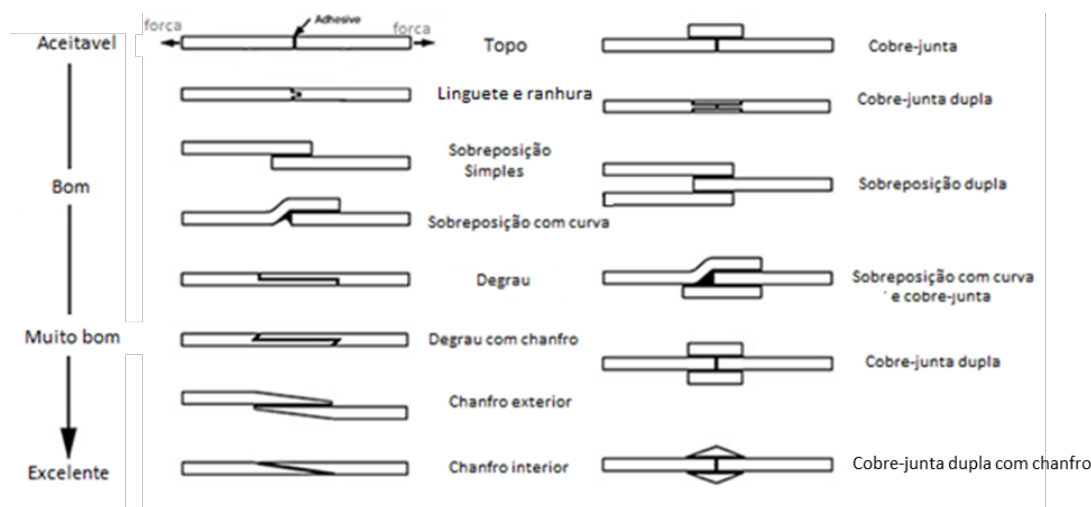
Tipos de ligações adesivas, adaptado de [18]
